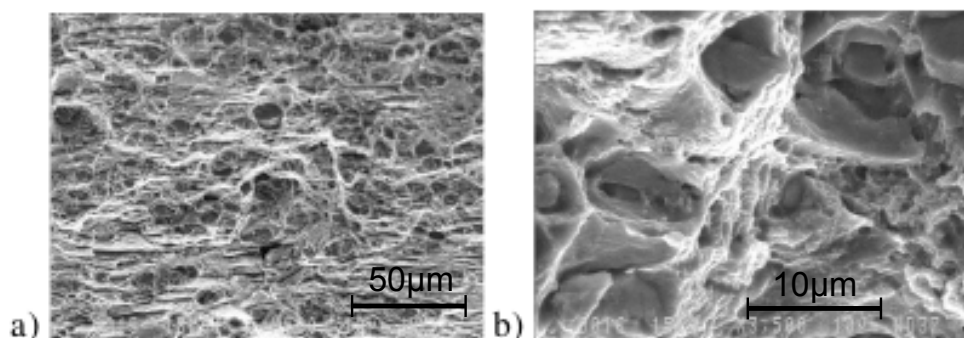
Observation MEB d'un faciès de rupture d'un joint soudé par FSW en alliage 7075-T6 après essai de traction monotone quasi-statique [66]
